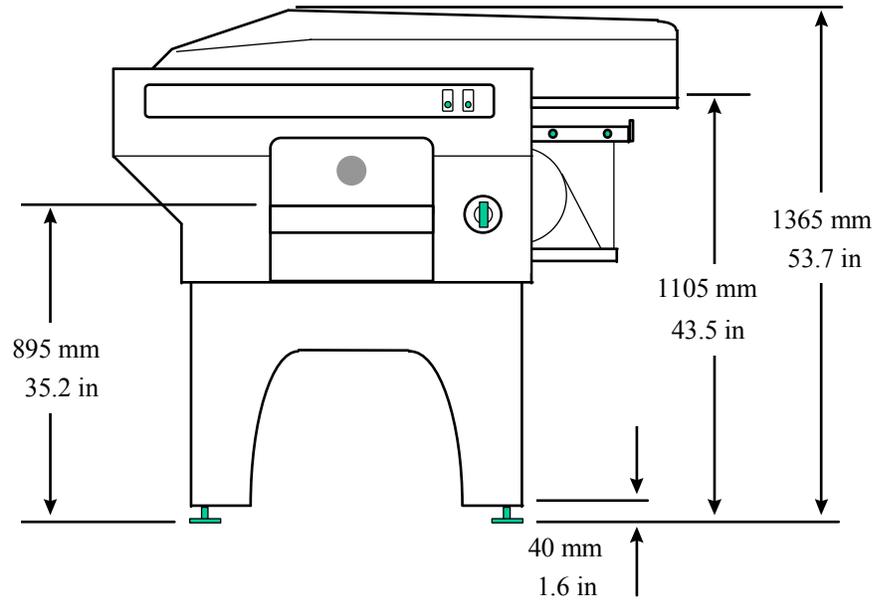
Dimensions SOLO™ Plus (Vue latérale)
